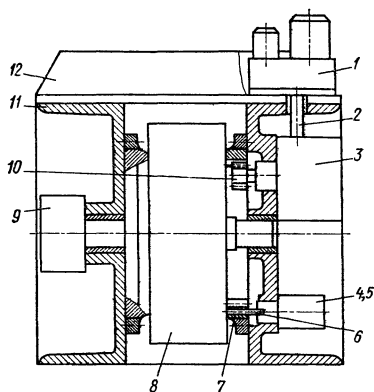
Компоновка барабанного приспособления с зубчатым приводом поворота: 1 — привод; 2 — вал; 3 — червячный редуктор; 4 — узел фиксации барабана; 5 — узел подклинки; 6 — палец фиксации; 7 — зубчатый венец; 8 — барабан; 9 — механизм осевого поджима барабана; 10 — приводное зубчатое колесо; 11 — стойка; 12 — портал
